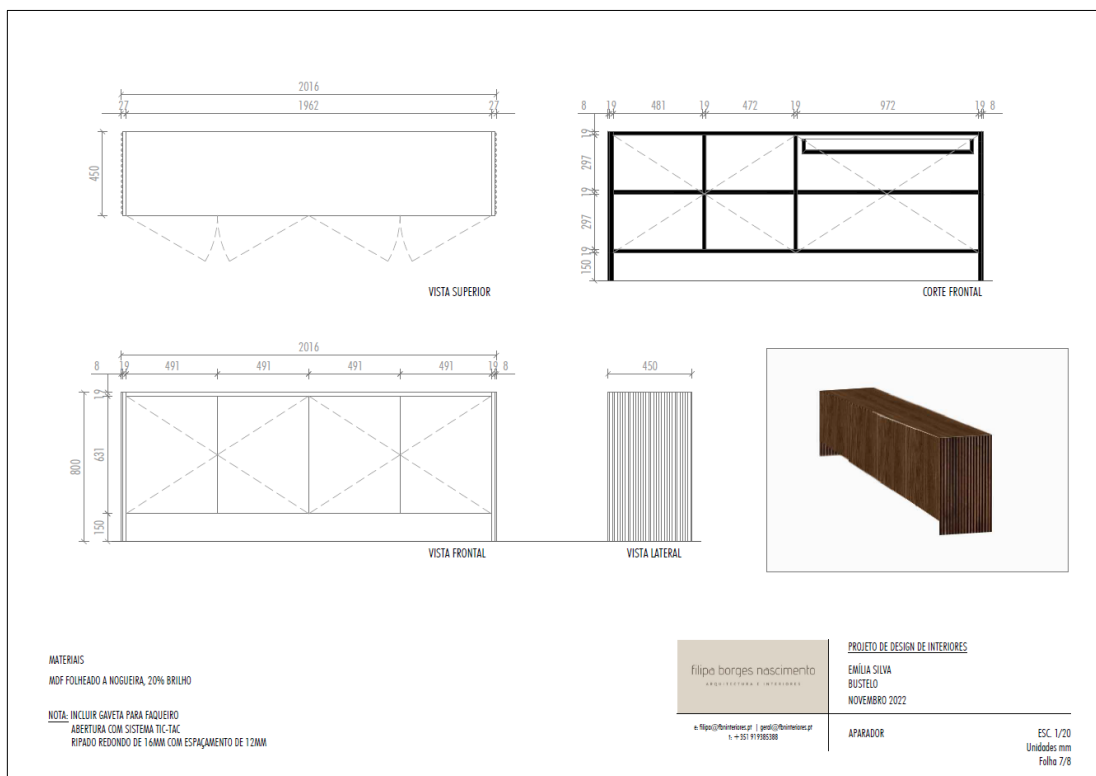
Desenho técnico de aparador - parte 1 (Fonte: Autora, 2022)
